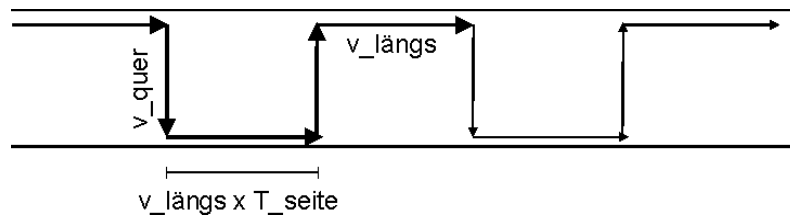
Schweißparameter Pendeltechnik
